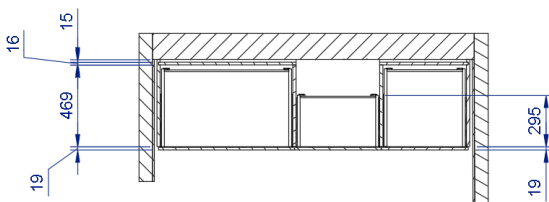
Desenho técnico de um corte em que representa o encolher da gaveta do meio. Fonte: Autora
